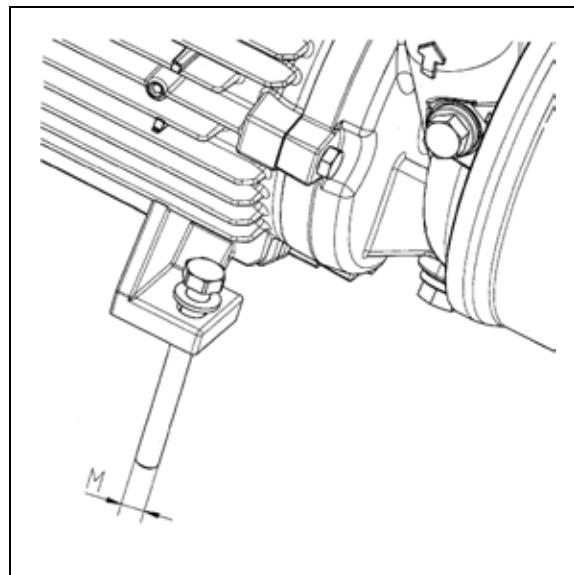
Befestigungselemente zum Verschrauben der Füße mit dem Untergrund
